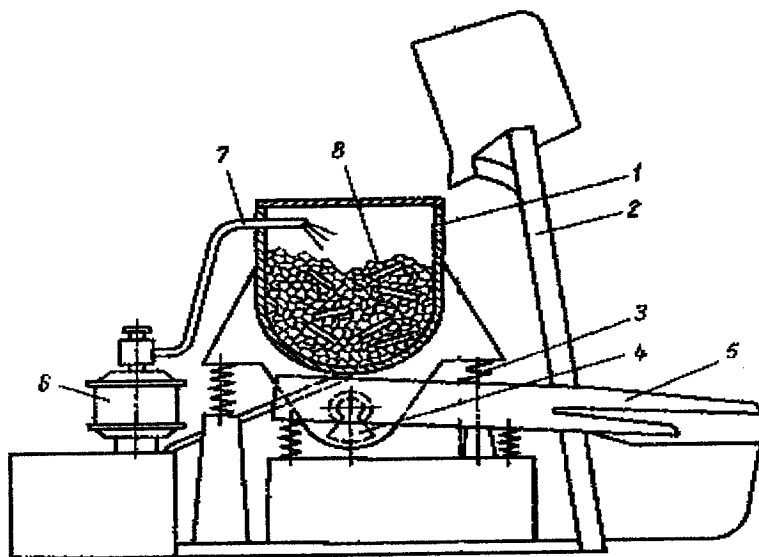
Схема установки для вібраційної обробки інструмента:
